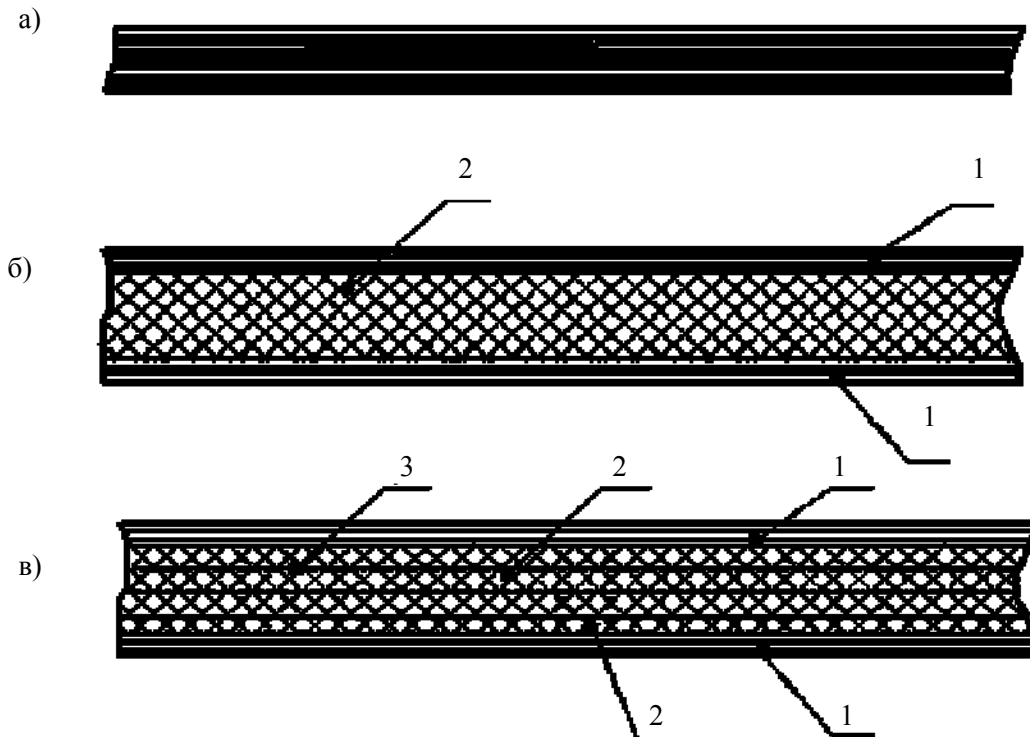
Конструктивні схеми обшивки корпусу (настилів палуб і полотниць перегородок) з ПКМ:
